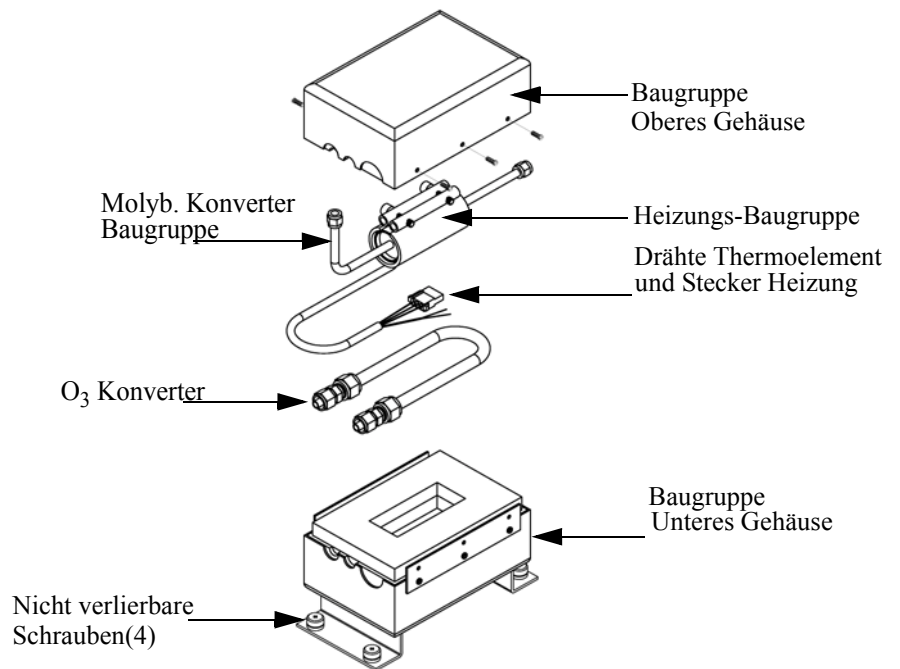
NO₂-NO Molybdän Konverter-Baugruppe
